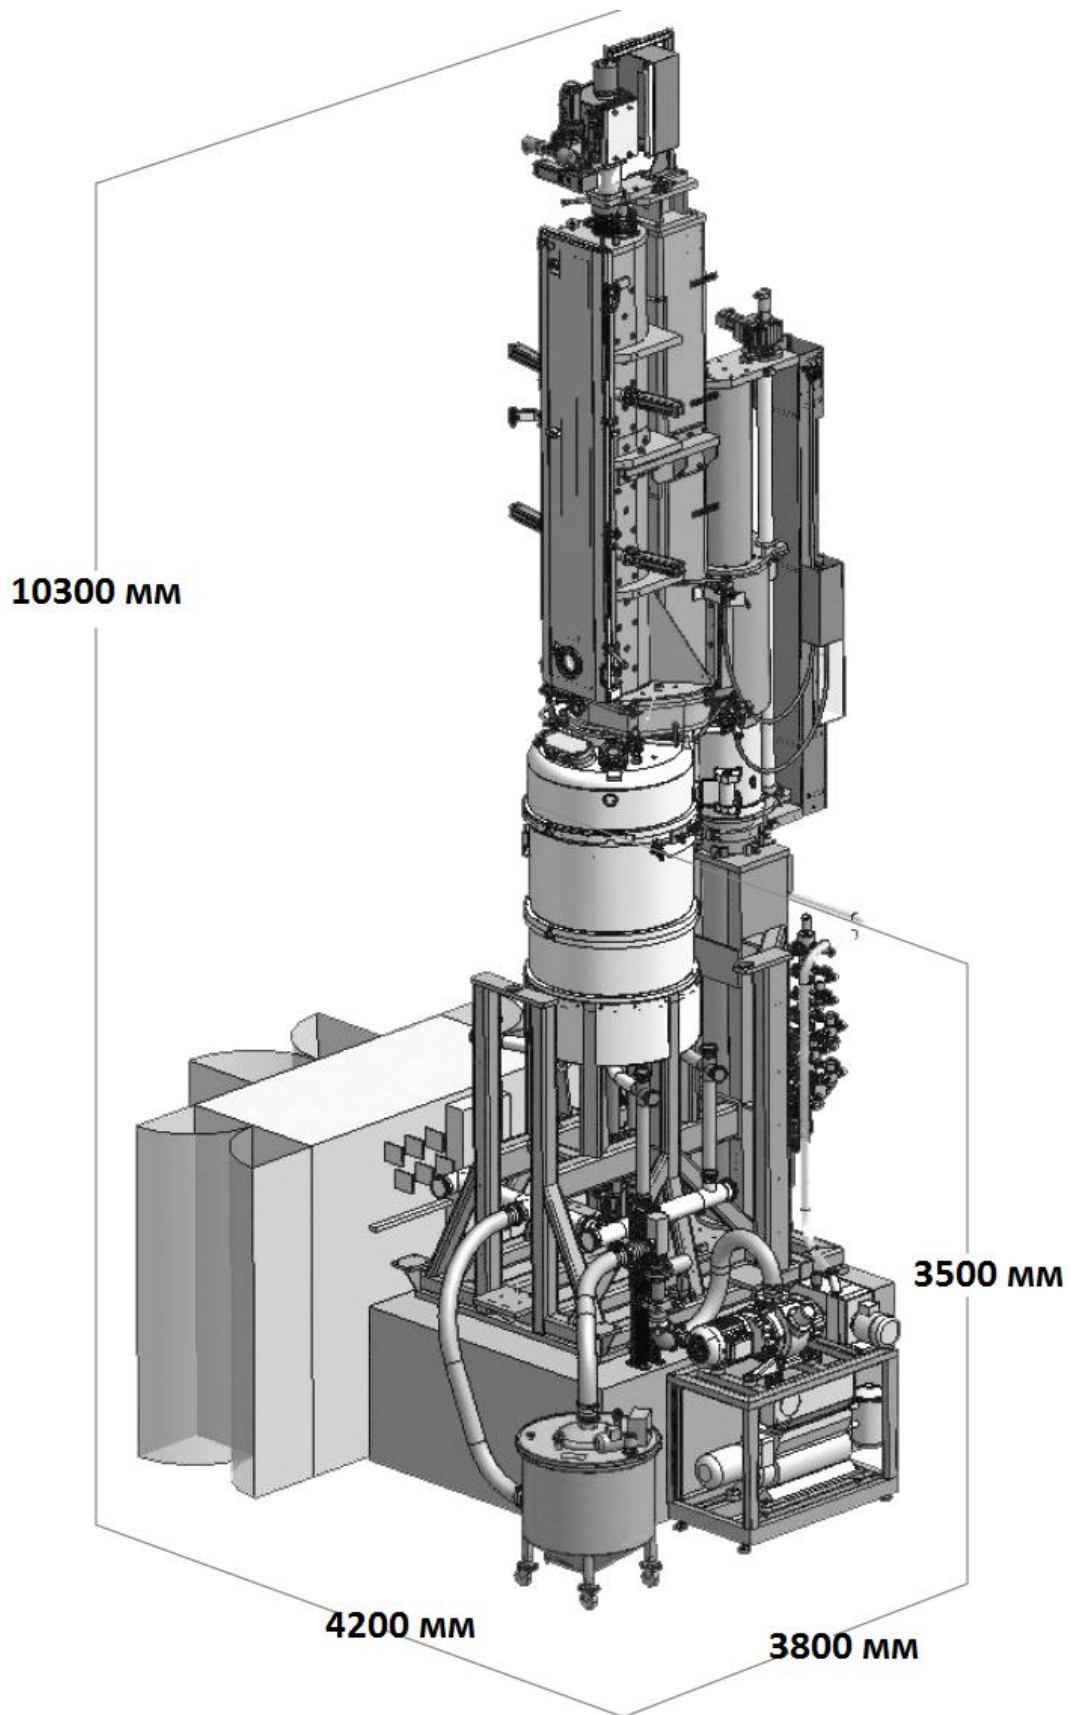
Установка EKZ-3500 компании PVA TePla AG [269], габаритный чертеж
